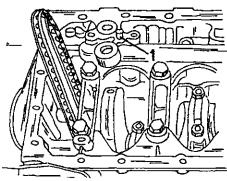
Расположение центрирующей втулки (1) в картере двигателя. Для наглядности двигатель показан с открытым картером.
